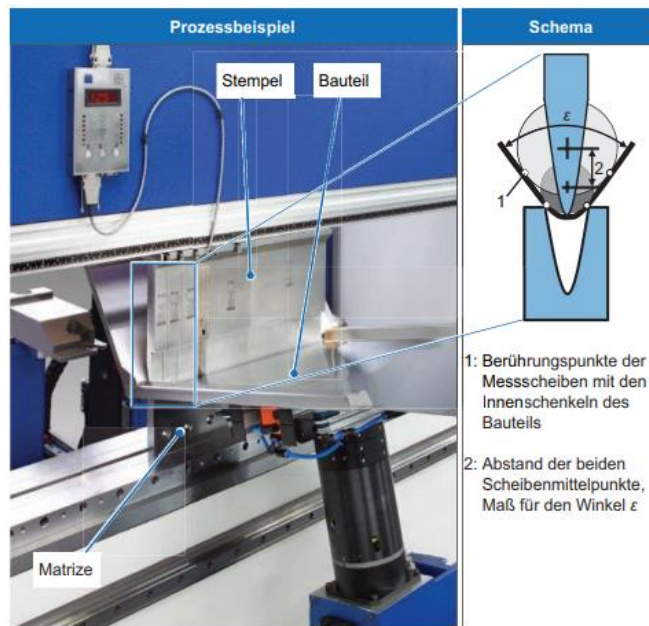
Werkzeug mit Messsystem ACB Wireless zur Biegewinkelerfassung
